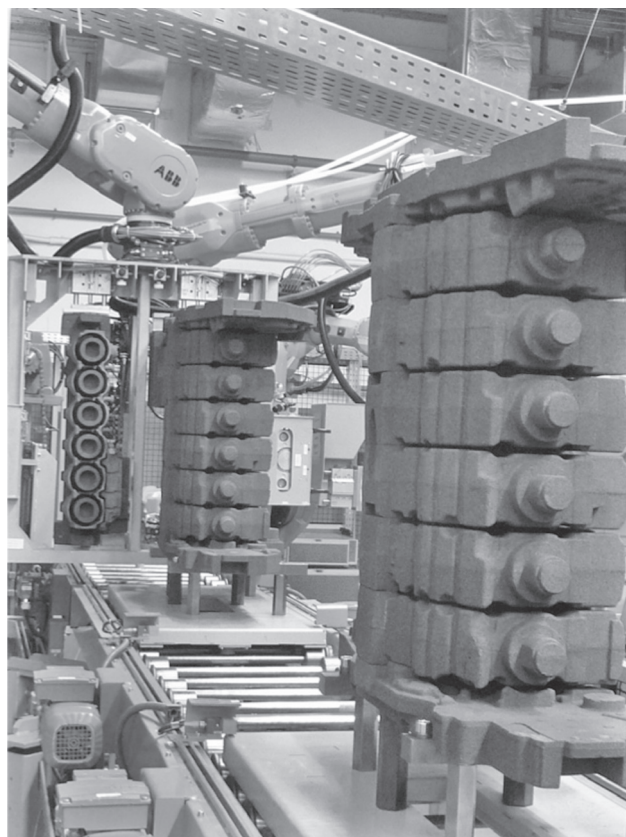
Роботизированный участок сборки стержней в двойные стержневые пакеты для получения отливок 6-ти цилиндрических грузовых двигателей. Завод *Daimler AG*, г. Мангейм, Германия
